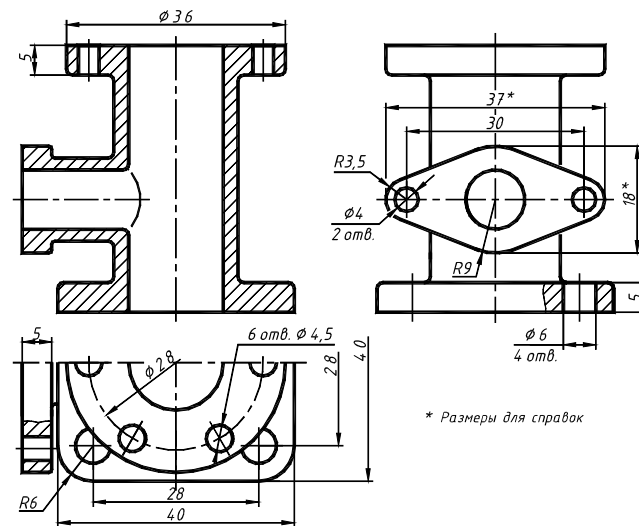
Изображения корпуса с проставленными размерами фланцев
